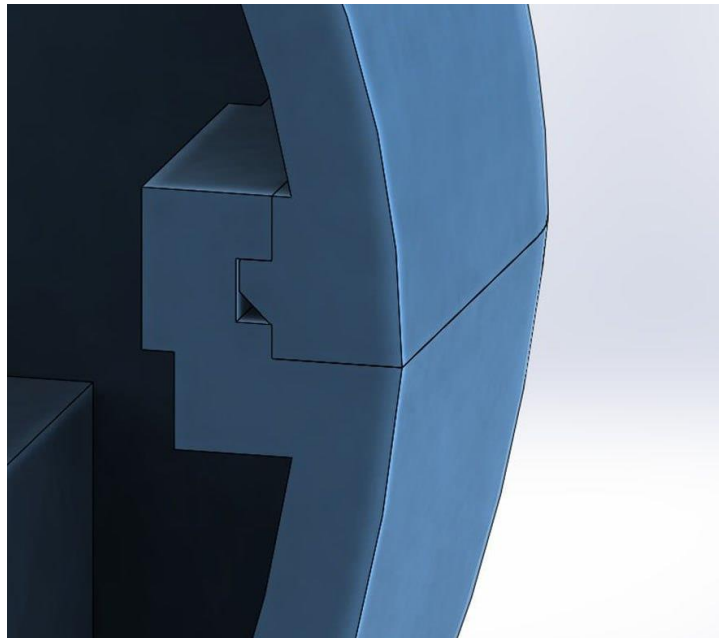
Тип з'єднання верхньої та нижньої кришок корпусу
